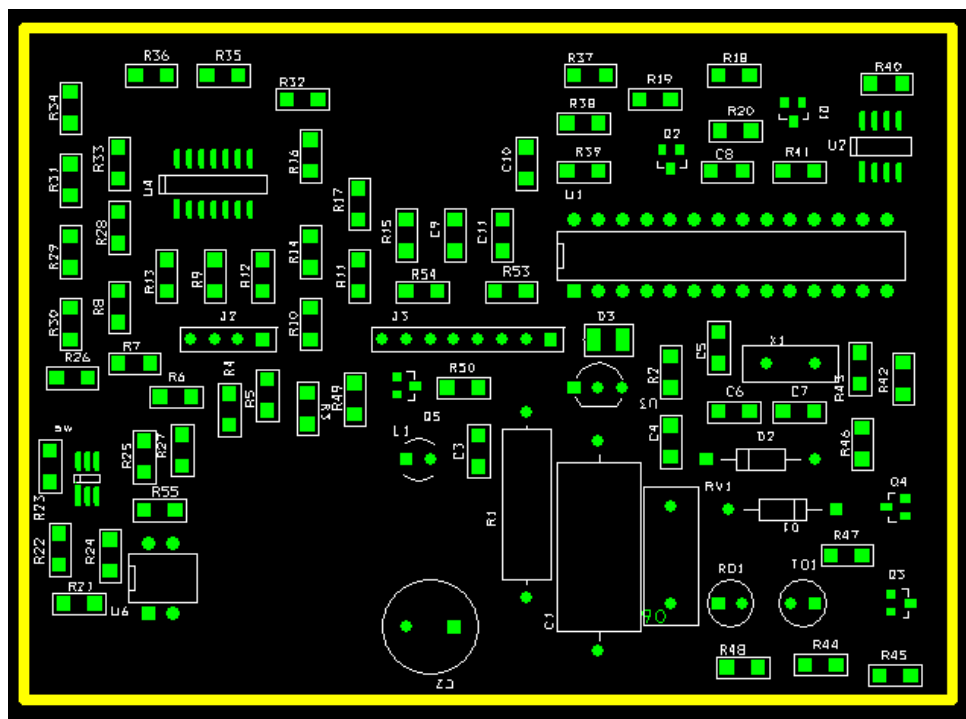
Tarjeta electrónica del metro contador, Silkscreen.
